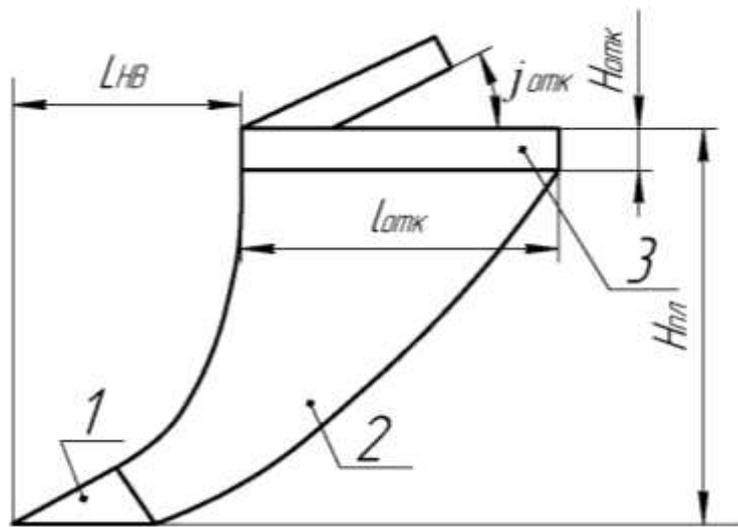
Схема параметров плужного каналкопателя: 1 – лемех, 2 – корпус, 3 – открылок
